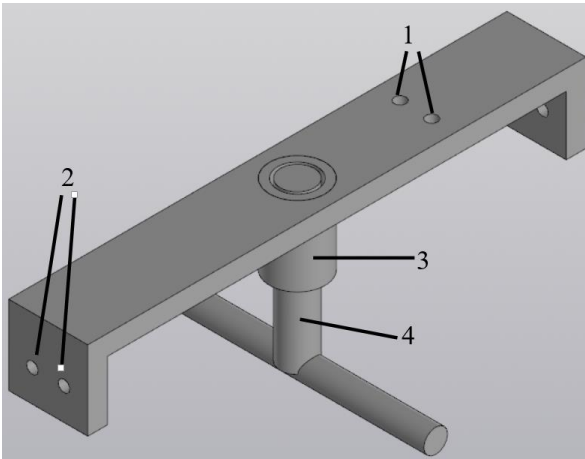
Конструкция измерительного механизма: 1 – отверстия для крепления тензодатчика; 2 – отверстия для крепления к установке; 3 – направляющая трубка поплавка; 4 – подвижный поплавок
